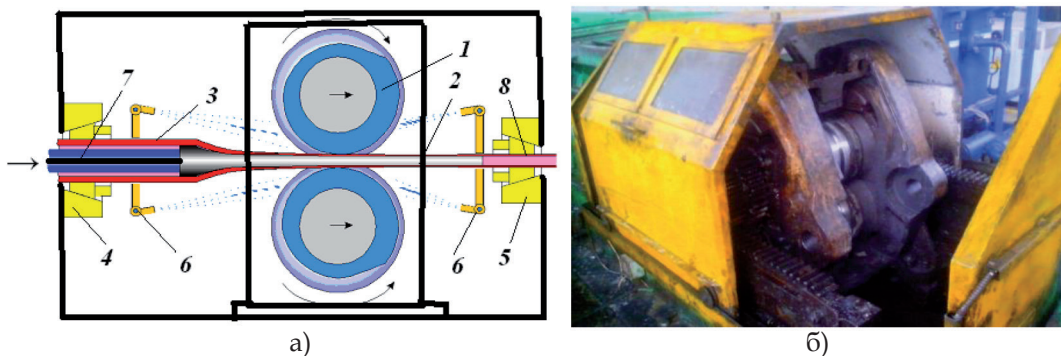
Система подачи технологической смазки и СОЖ на поверхности ручья и рабочего конуса а) и рабочее пространство клетки стана ХПТ 32:
